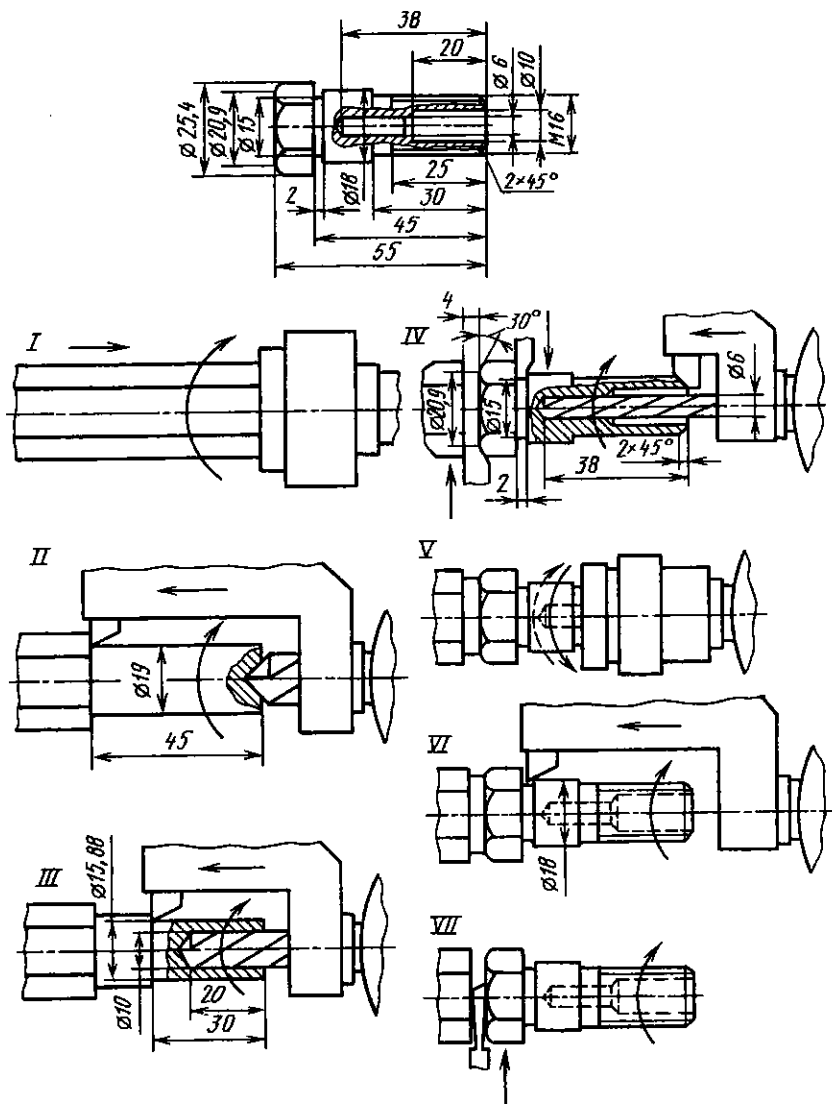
Схема обработки детали на токарно-револьверном автомате:
